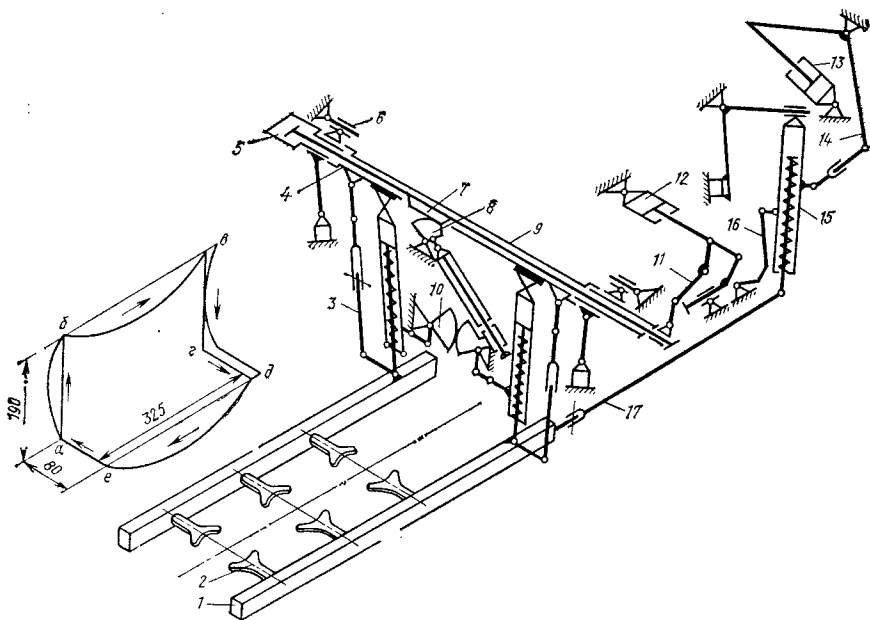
Кинематическая схема грейферного переключника с гидравлическим приводом: 1 — балка; 2 — захват; 3 — тяга привода подъема и опускания балок; 4 — корпус; 5 — гидроцилиндр привода сближения и удаления балок; 6 — шарнир механизма подъема и опускания; 7 — рейка; 8 — зубчатый сектор; 9 — тяга; 10 — секторы привода сближения и разведения балок; 11 — тяги; 12 — гидроцилиндр привода продольной подачи балок; 14 — шарнир; 15 — демпфер; 16 — ограничитель хода; 17 — тяга
